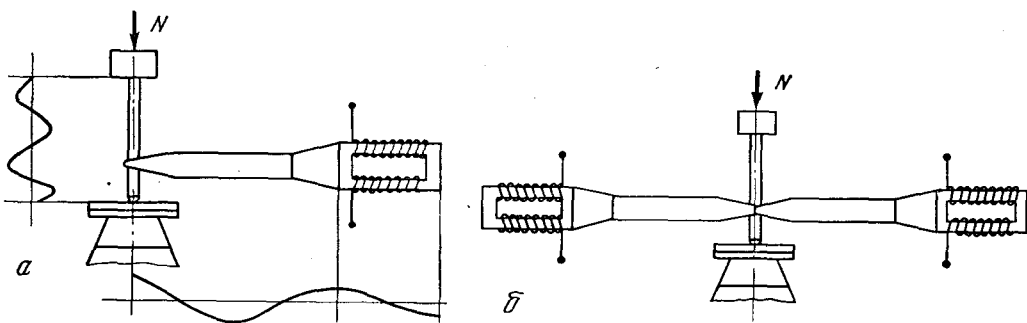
Продольно-поперечные колебательные системы для сварки
